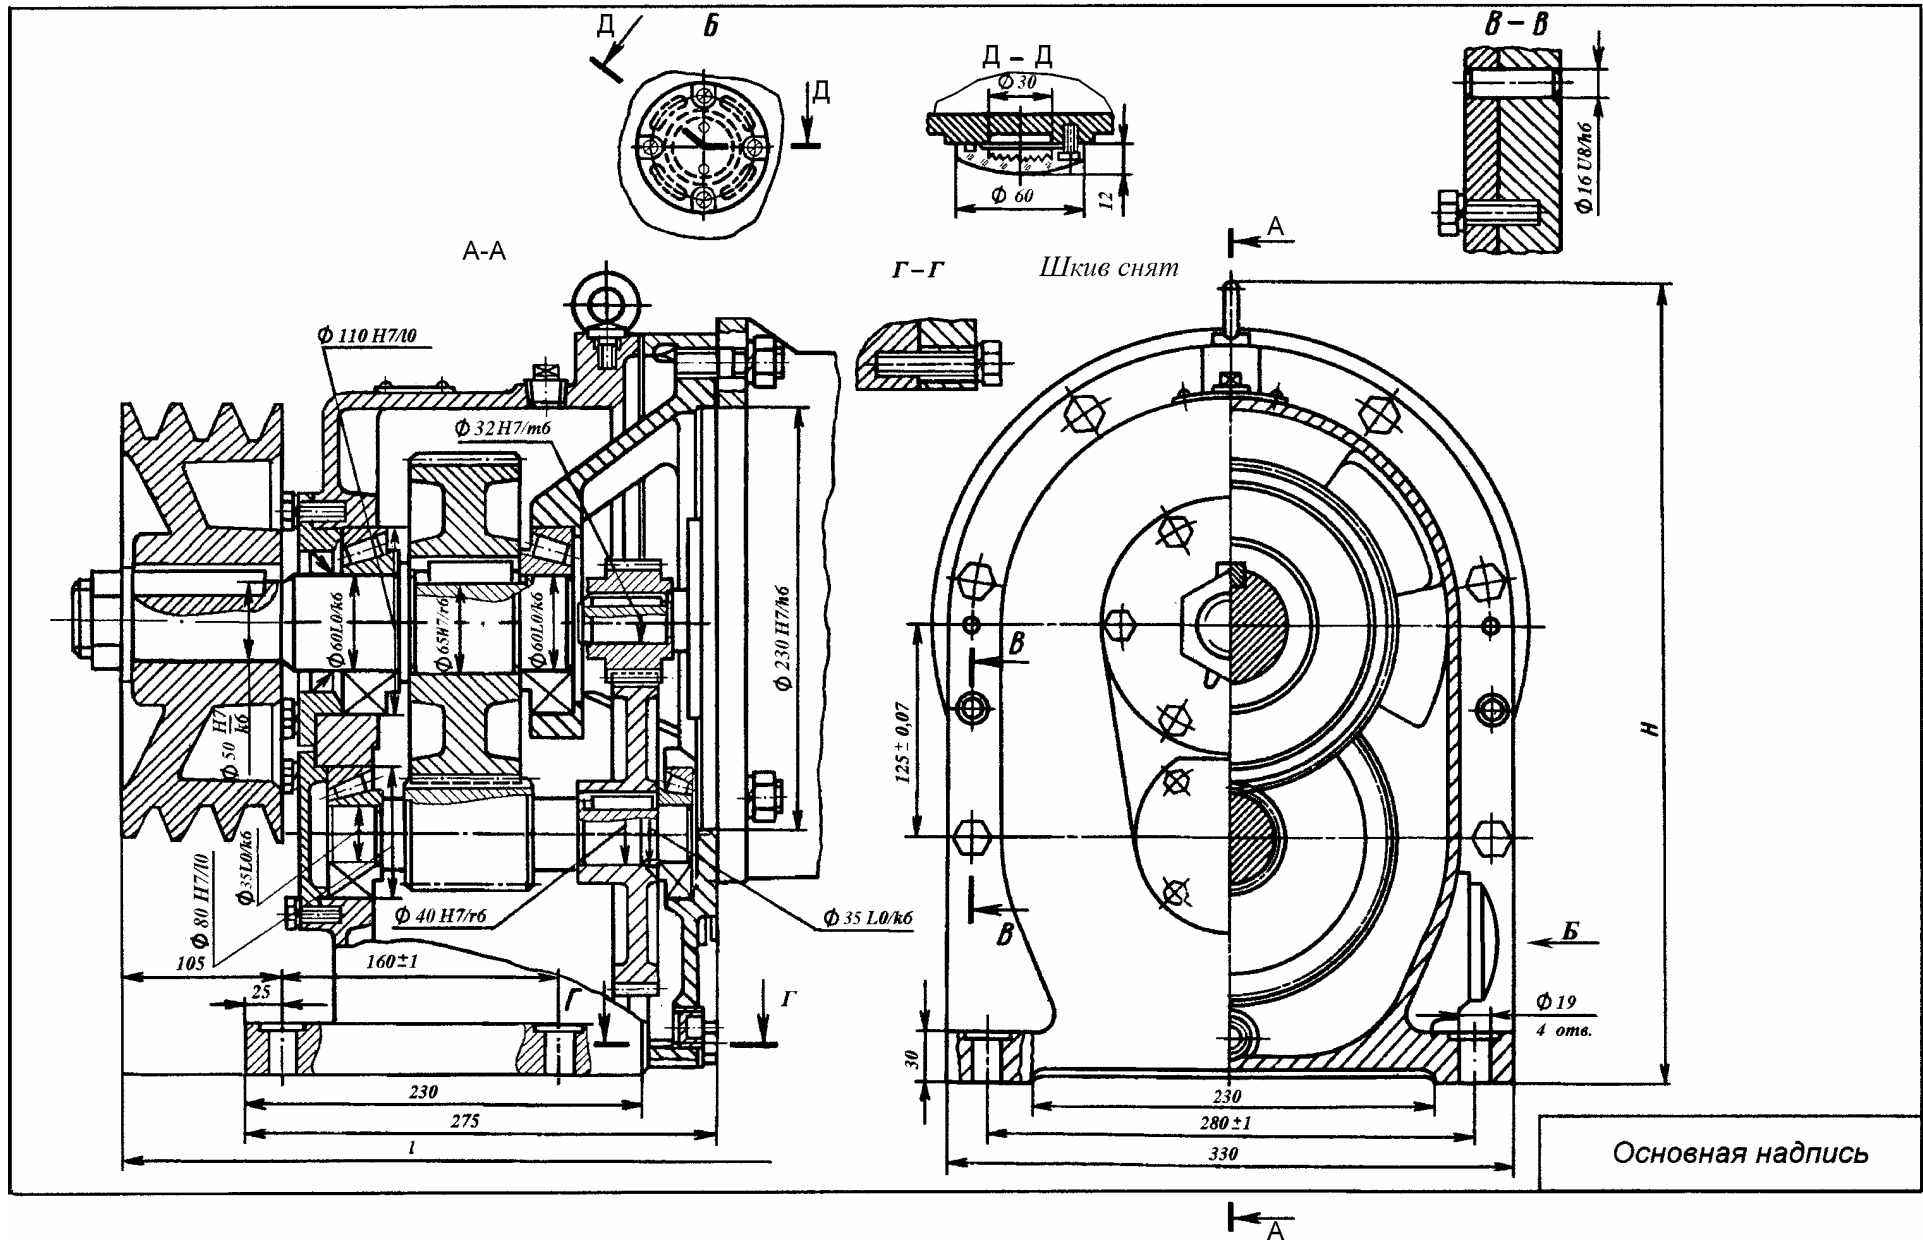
Редуктор цилиндрический двухступенчатый с фланцевым электродвигателем (развертка и свертка)
